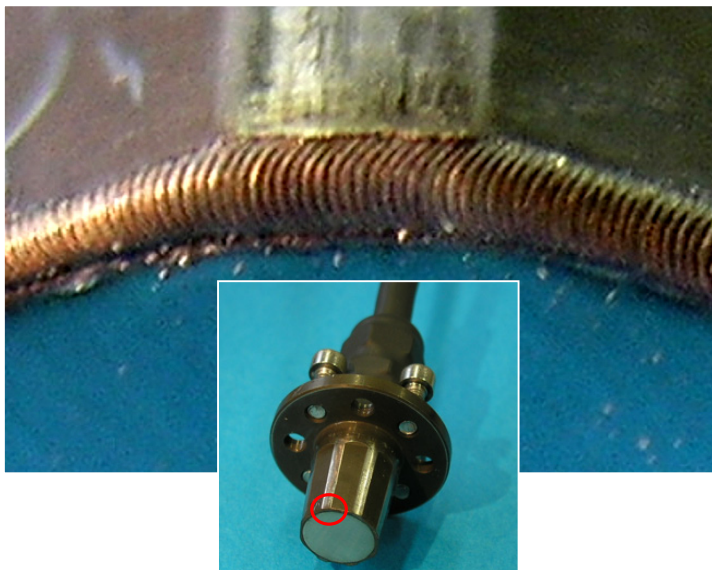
Mittels Laser aufgeschweißte Stahlmembran an der Spitze des Sensors.
